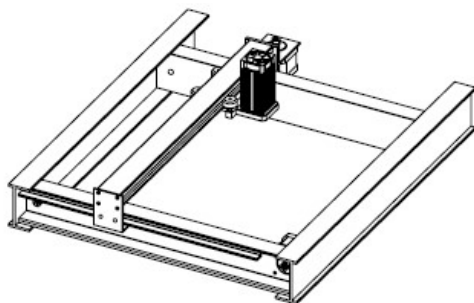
Загальний вигляд пристрою для лазерної різки матеріалів
